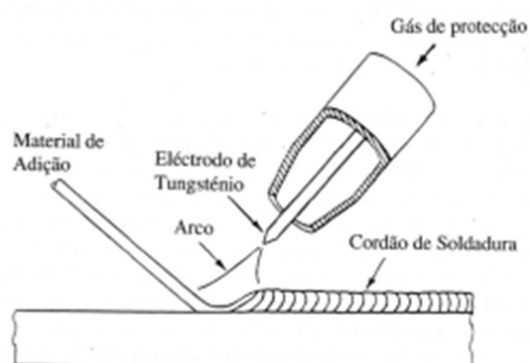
Processo de soldadura TIG⁸⁶
